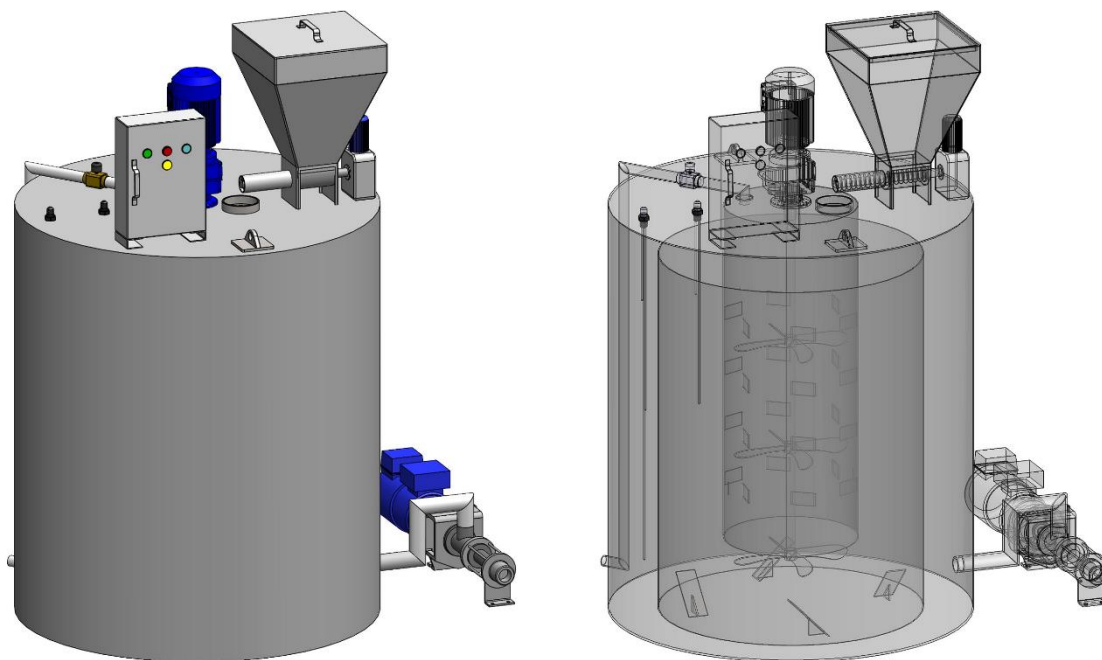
3D-модель автоматической мехатронной установки для приготовления флокулянта.
